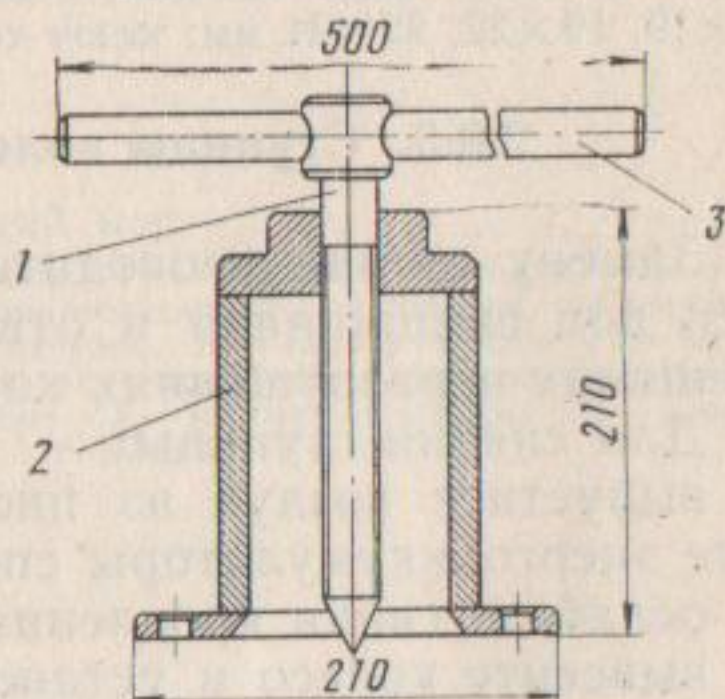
Приспособление для снятия ступицы переднего колеса:
